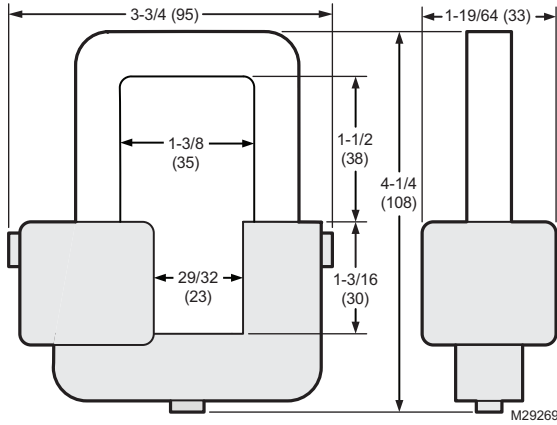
Dimensions du capteur de courant 400 A en po (mm).
